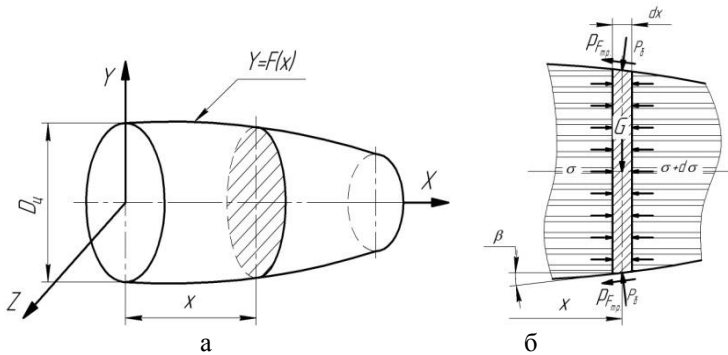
Схема дії сил на елементарний шар у конічній частині циліндроконічного корпусу
